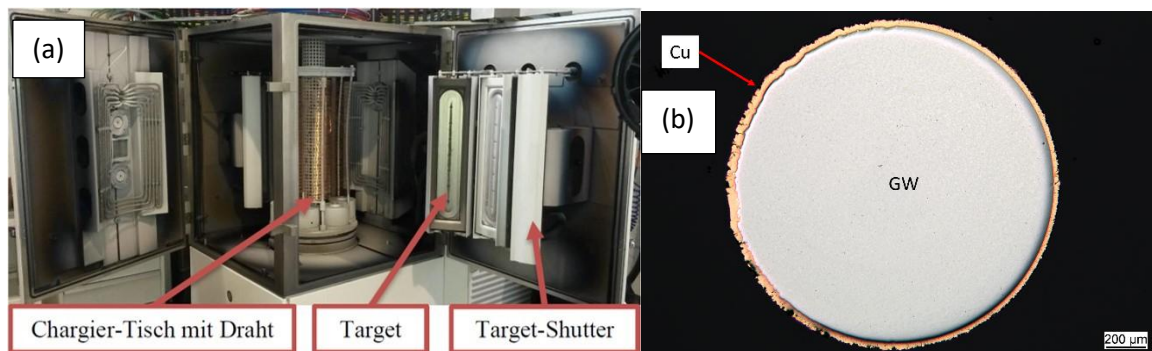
(a) Beschichtungsanlage (Magnetronspütern) mit Schweißzusatz und Beschichtungsmaterial (Target) des Instituts für Schweißtechnik und Trennende Fertigungsverfahren der TU Clausthal [244]; (b) Querschliff eines Schweißzusatzwerkstoffs, beschichtet mit Cu für 6h (lichtmikroskopische Aufnahme).
